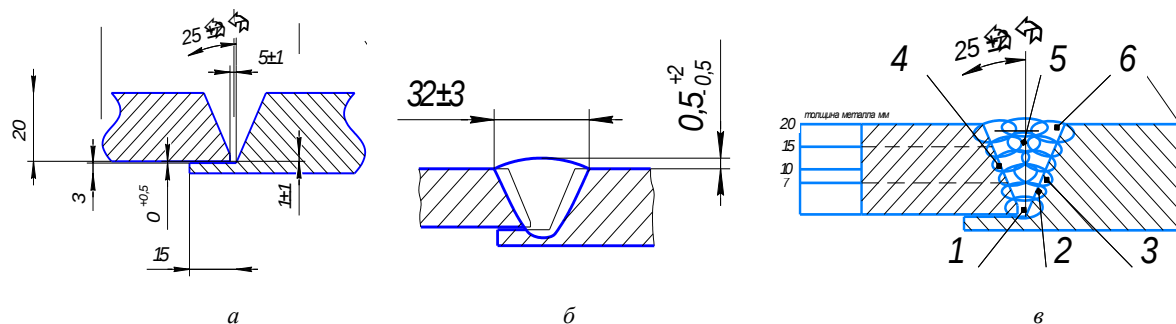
Конструктивные элементы при дуговой сварке плавящимся покрытым электродом:
